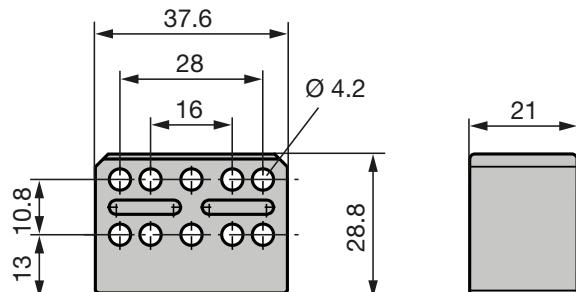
Medidas de montaje del sensor de posición BTL6-A-3800-2
